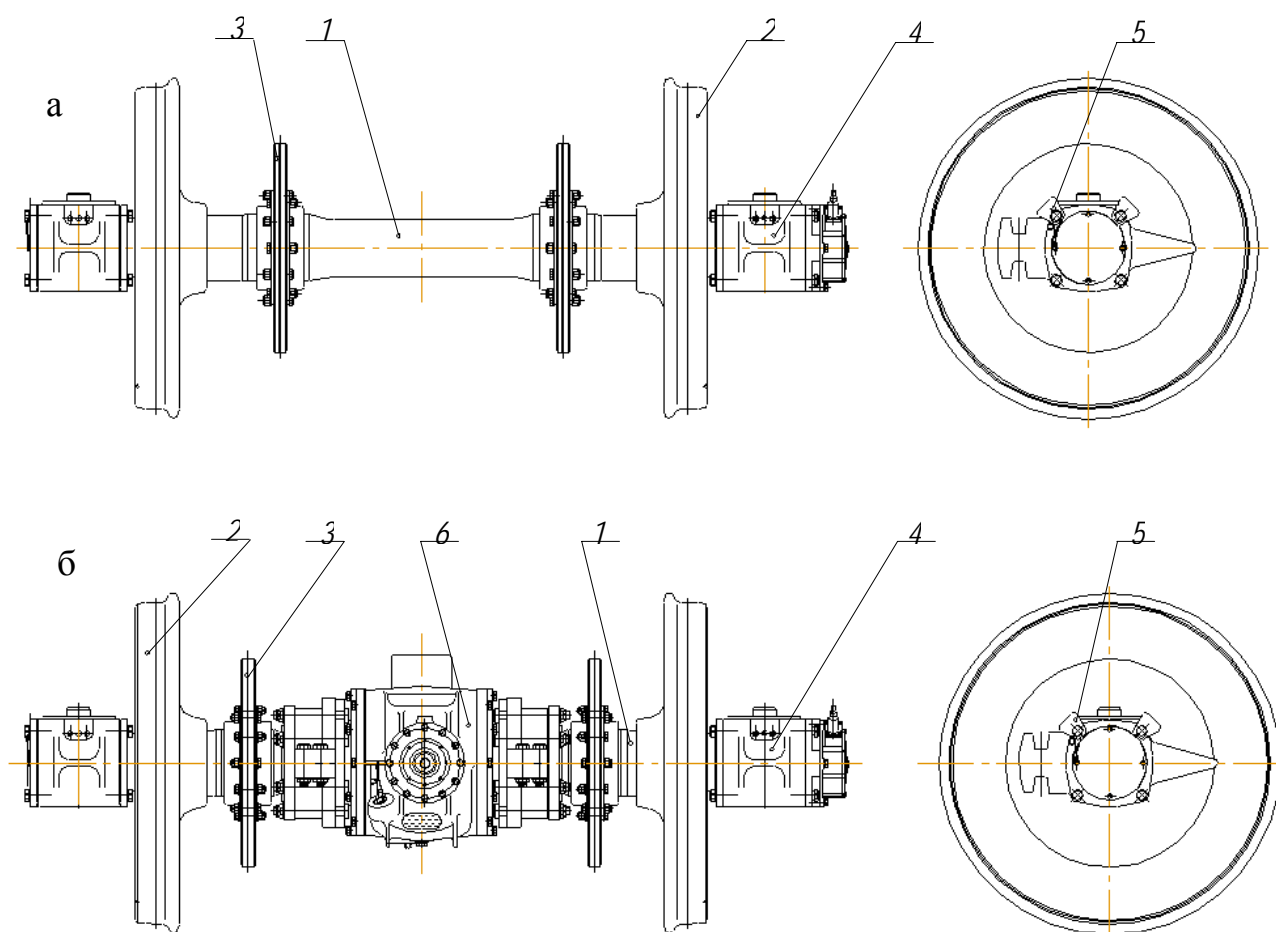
Колесные пары без редуктора а и с редуктором б
